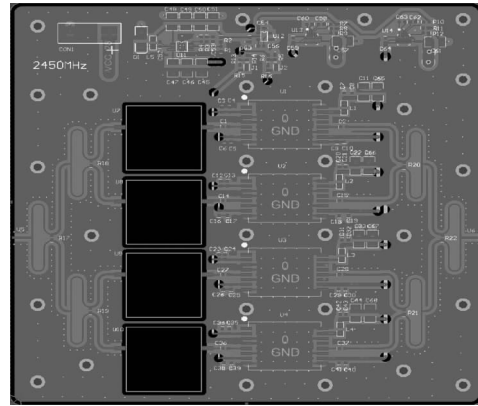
MAMG-100227-010C0L 末级功率放大器 PCB
